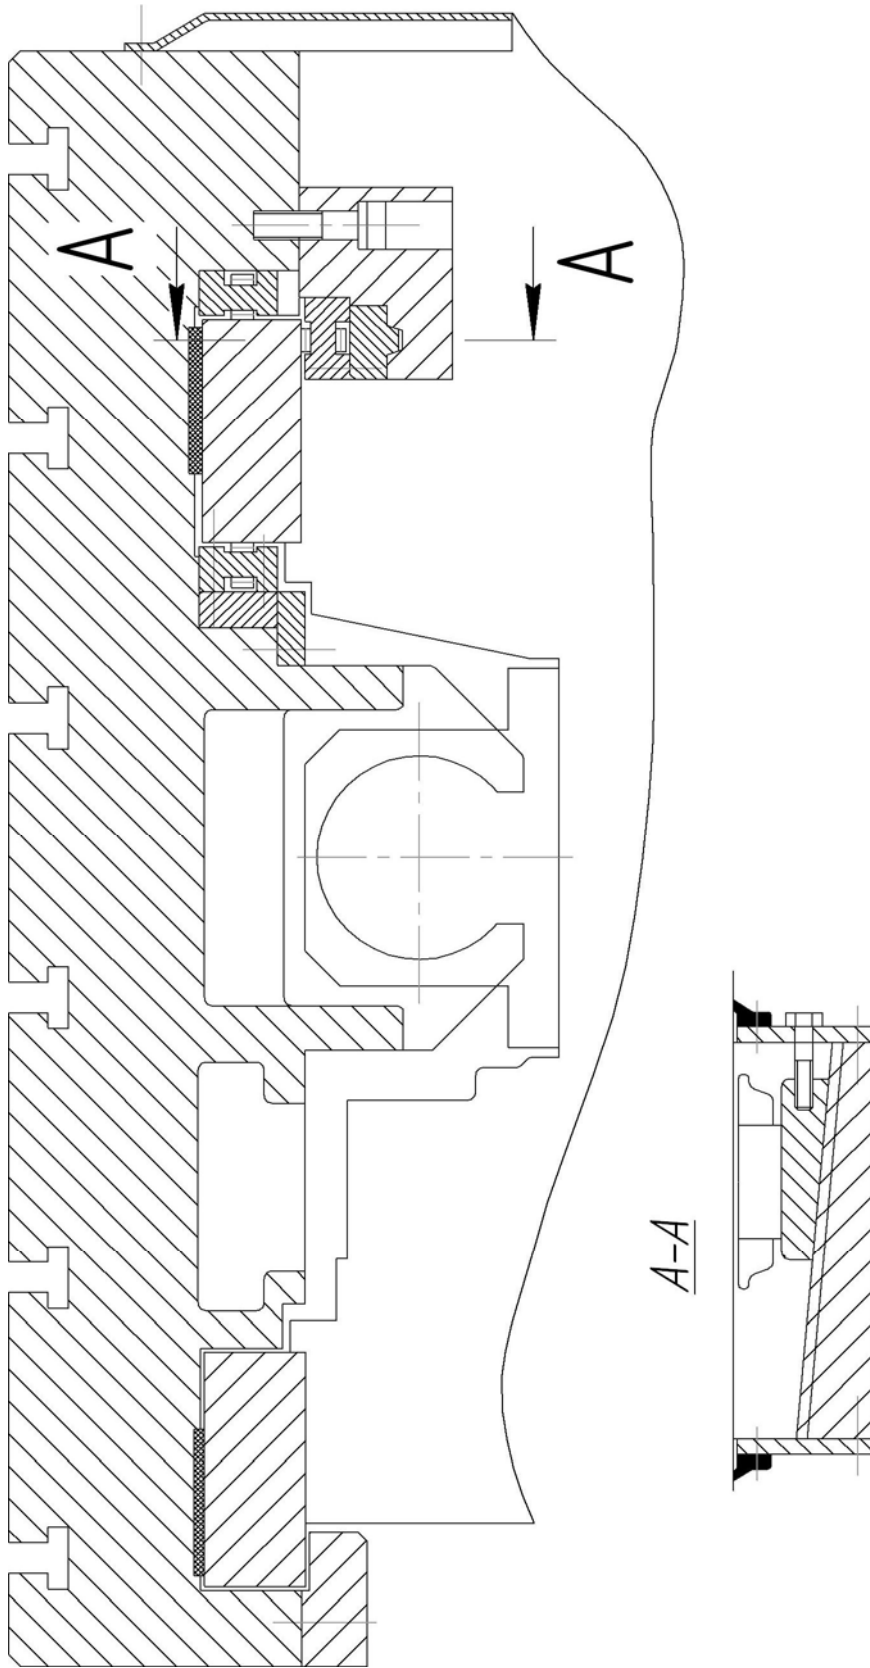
Пояснить основные особенности направляющих фрезерного станка с ЧПУ
